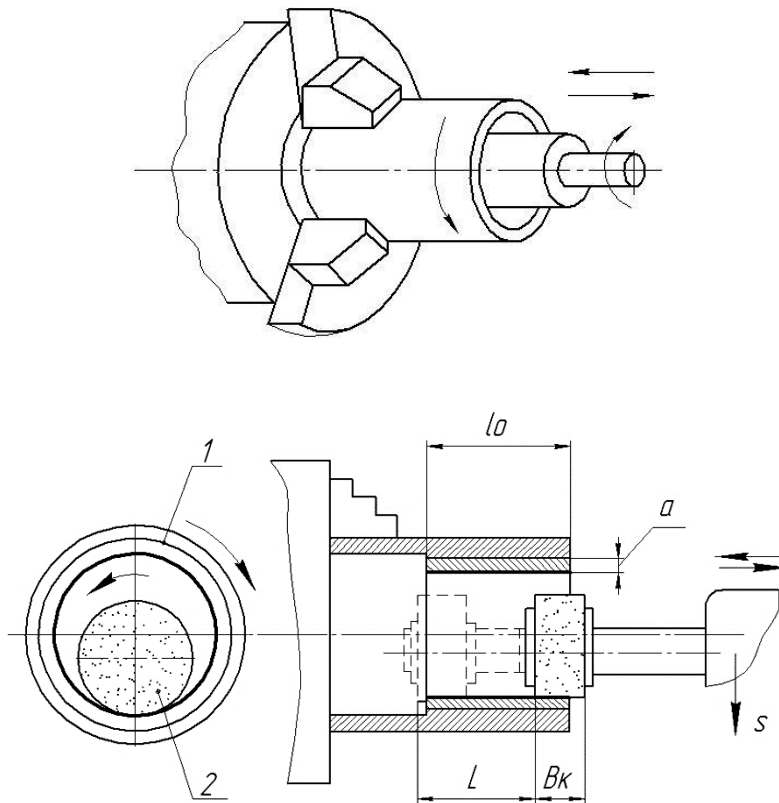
Схема оброблення отвору на внутрішньошліфувальному верстаті
